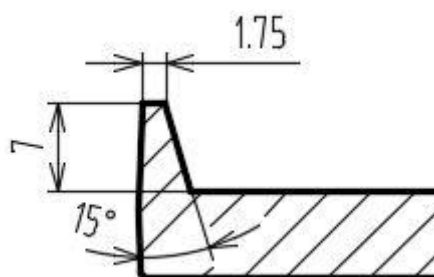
Inspirace základních rozměrů wingletu [10]
